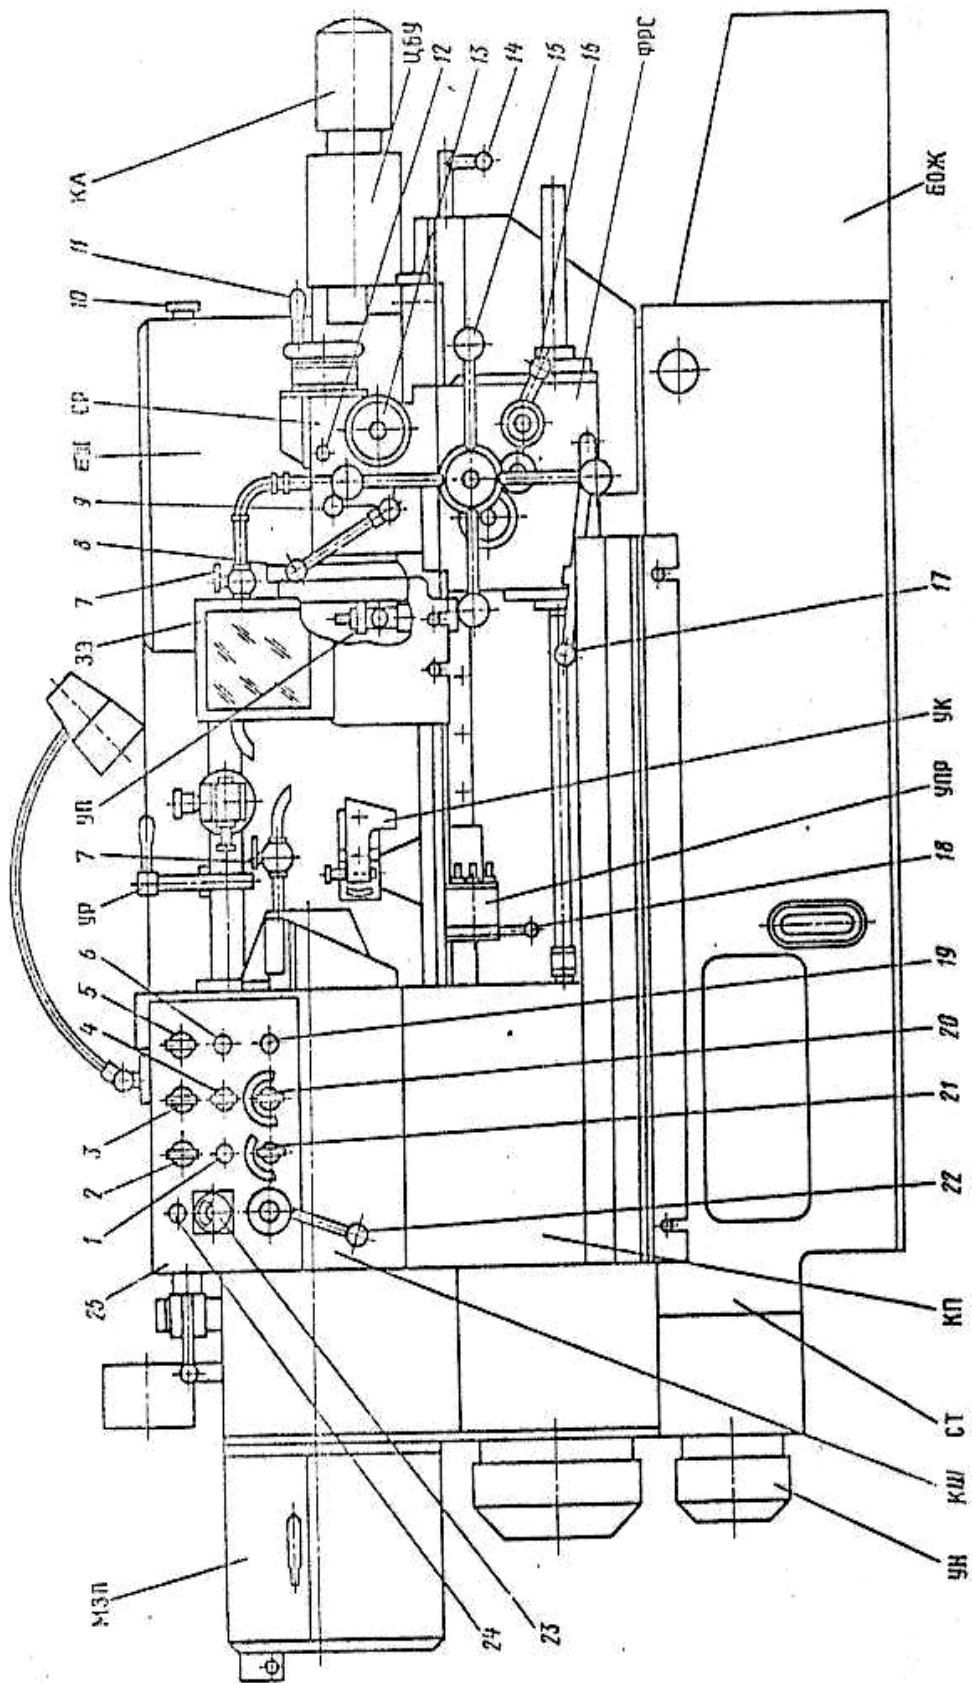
Основні частини та органи керування токарно-револьверного верстата модної 1К341
